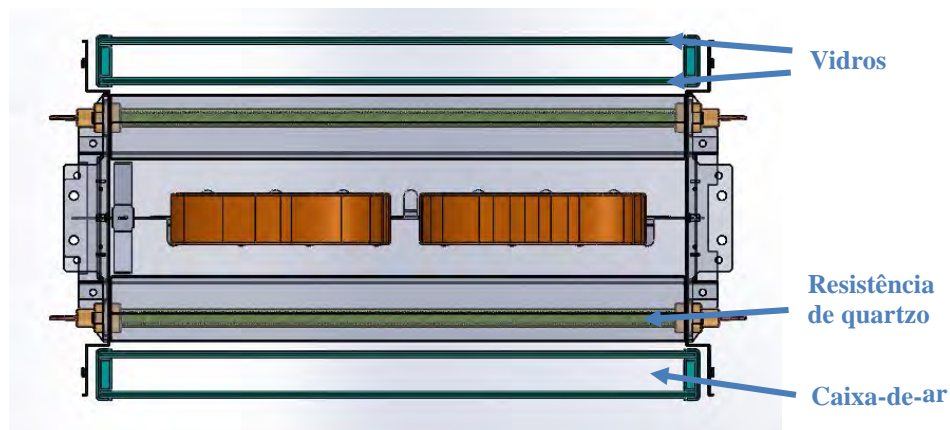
Vista de topo da estrutura da Torradeira de vidro.
